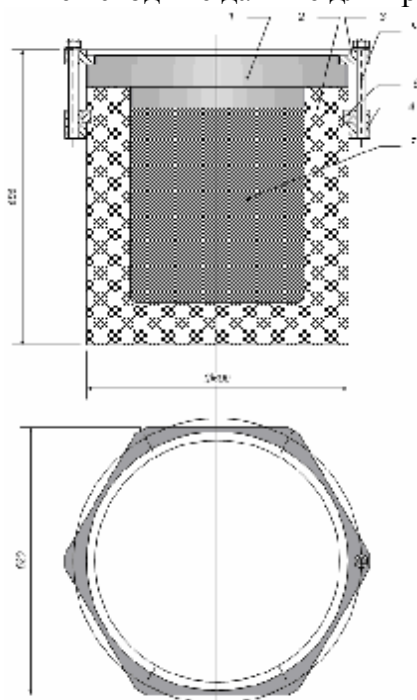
Конструкция керамического контейнера: 1 – крышка; 2 – корпус; 3 – фланец; 4 – фланец; 5 – кольцо разрезное; 6 – шпилька; 7 – РАО
